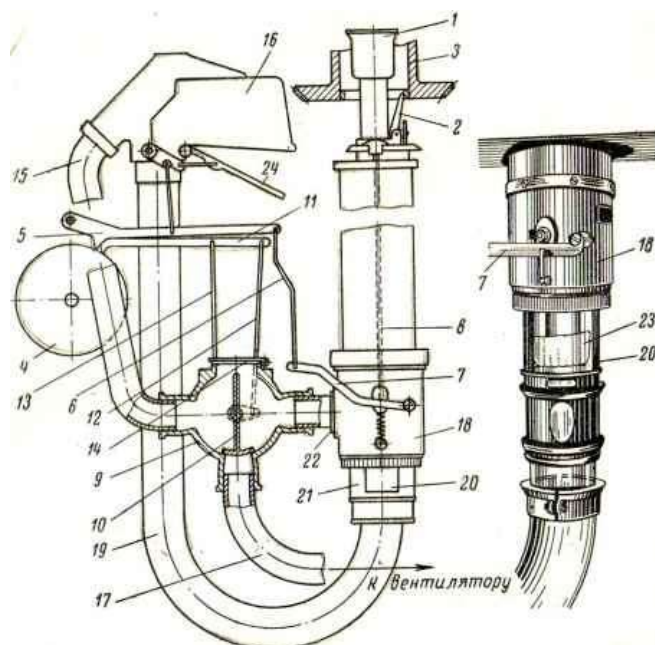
Механизм пневматической оттяжки с автоматической вывороткой изделия
